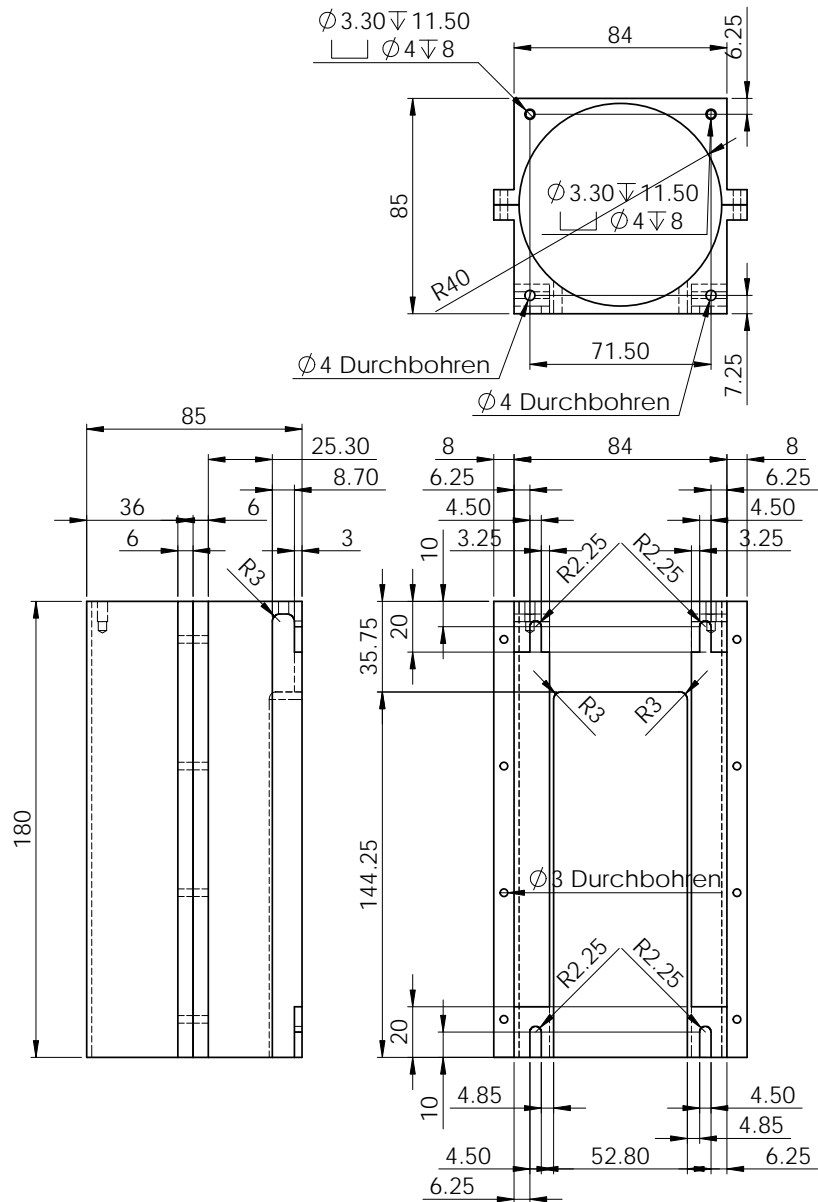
Technische Zeichnung der Kühlhaube der Röntgenröhre.
